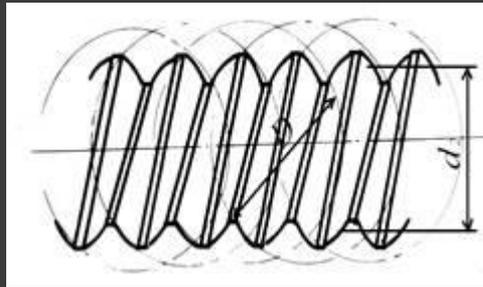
Резьбовой ролик: d_2 – средний диаметр резьбы; D_w – приведенный диаметр резьбы
